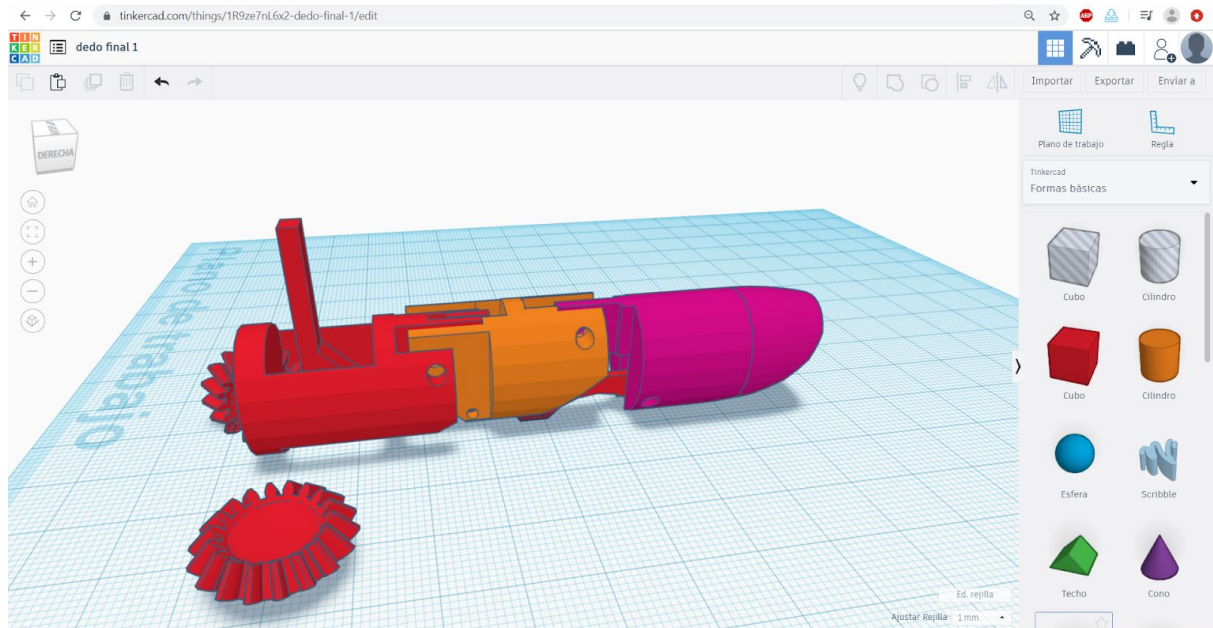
Dedo completo con engranaje cónico de dientes rectos.
